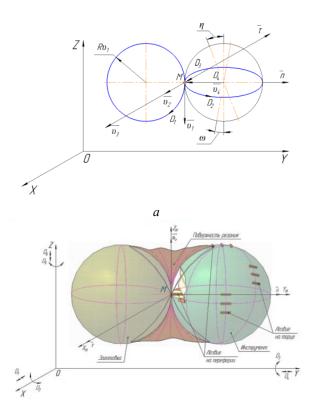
Схема комплексной обработки резанием: а – кинематическая схема, б – схема обработки
